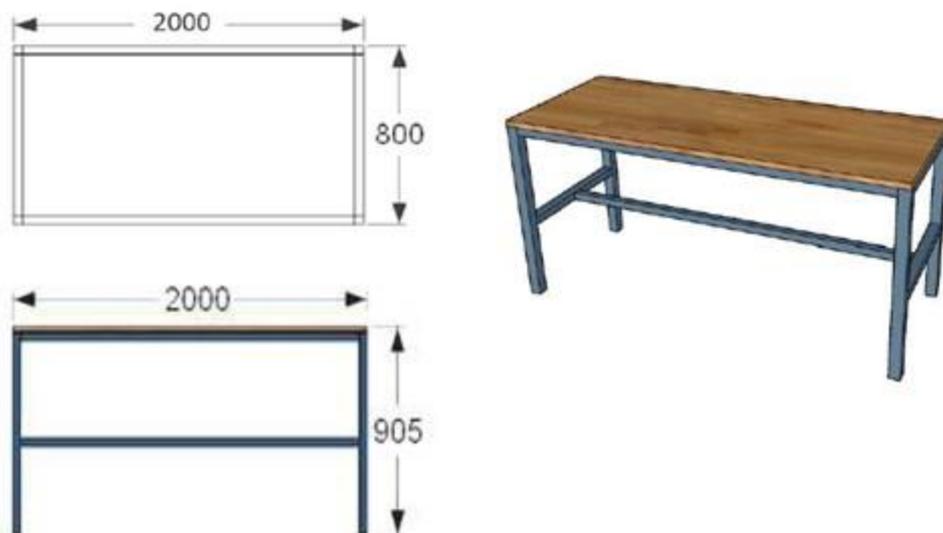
Planta baixa, vista frontal e perspectiva modelo item 27
